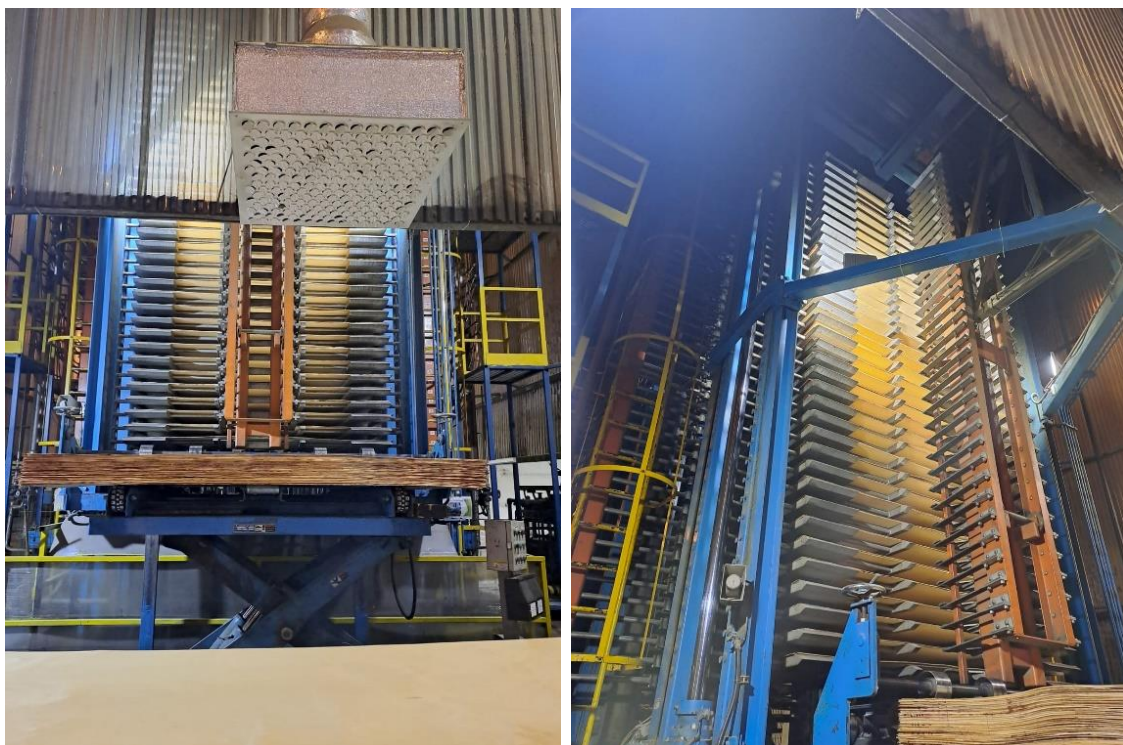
Универсальный 35 этажный горячий пресс для прессования большеформатной фанеры Kitagawa, Япония (размеры плит 1,4×2,8 м)
